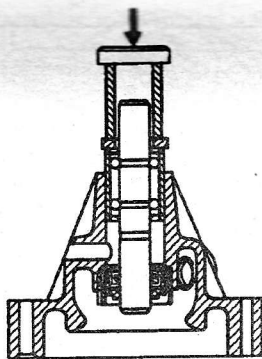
Запрессовка подшипника с валом водяного насоса в корпусе
